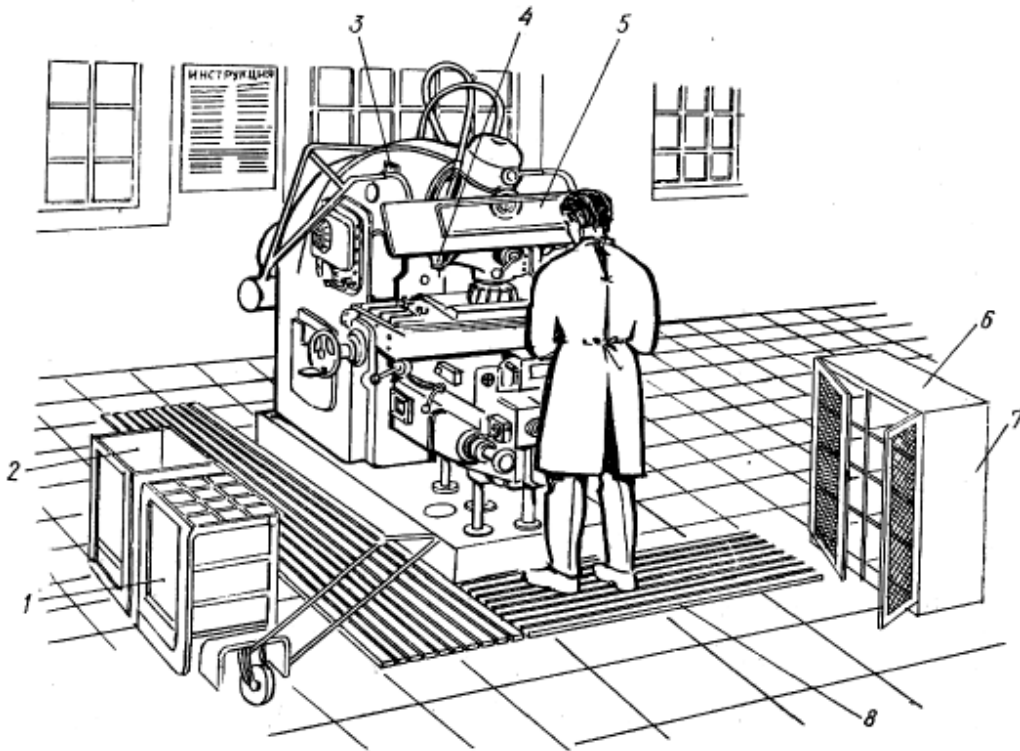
Робоче місце фрезерувальника: 1 – ящик для деталей; 2 – ящик для заготовок; 3 – верстат; 4 – лампа місцевого освітлення; 5 – захисний екран; 6 – верхня площина шафи для розміщення робочих креслень; 7 – інструментальна шафа; 8 – поміст
